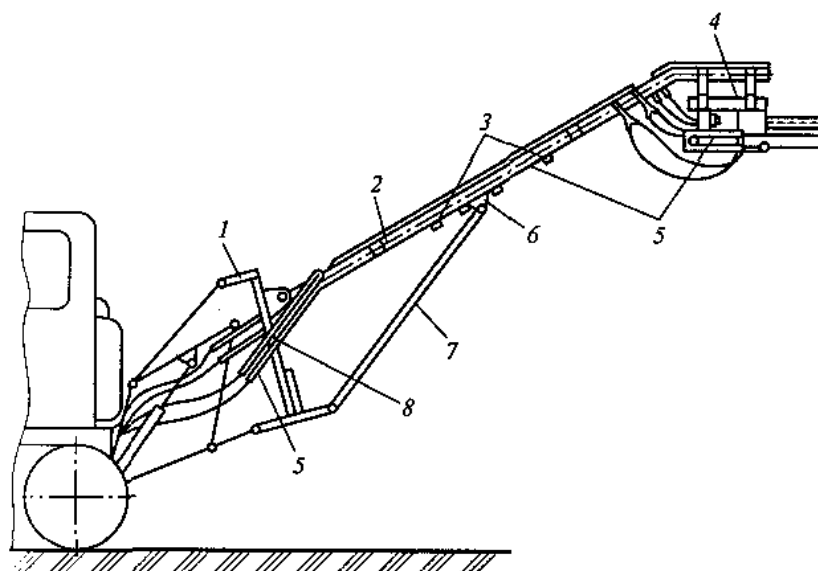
Машина для сбора ореха МСО-0,4:
